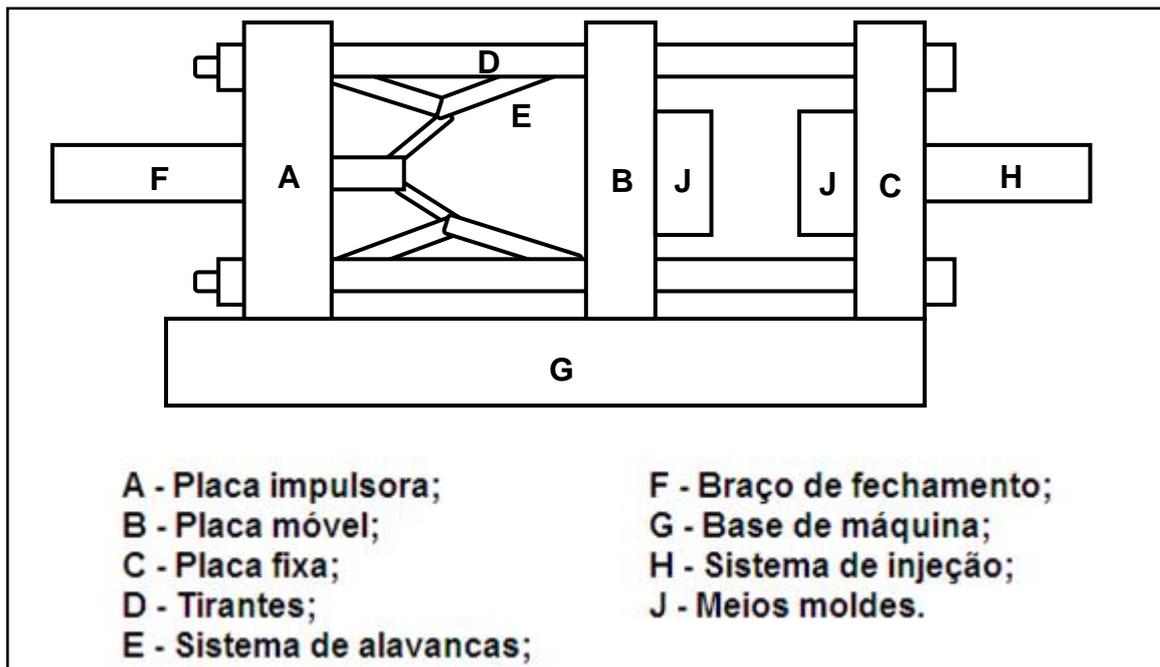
Componentes do dispositivo mecânico de fechamento de uma máquina injetora – ADAPTADO de [7]
